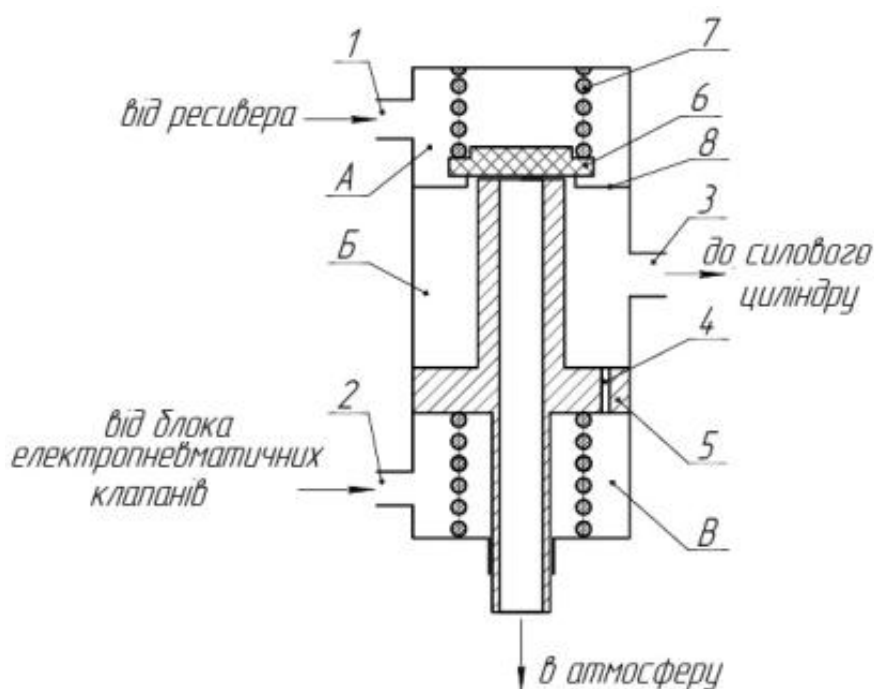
Принципова схема розробленого прискорювального клапана
